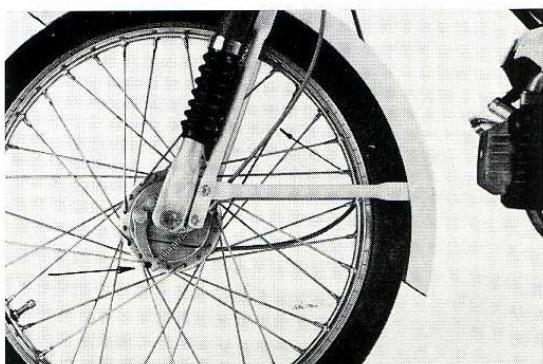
DEMONTAGE DU CABLE DU FREIN AVANT.
